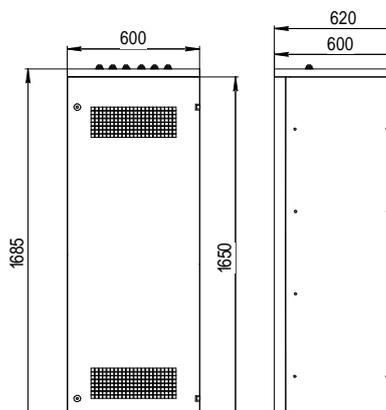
Габаритный чертеж шкафа аккумуляторного УЭПС-2 А3
